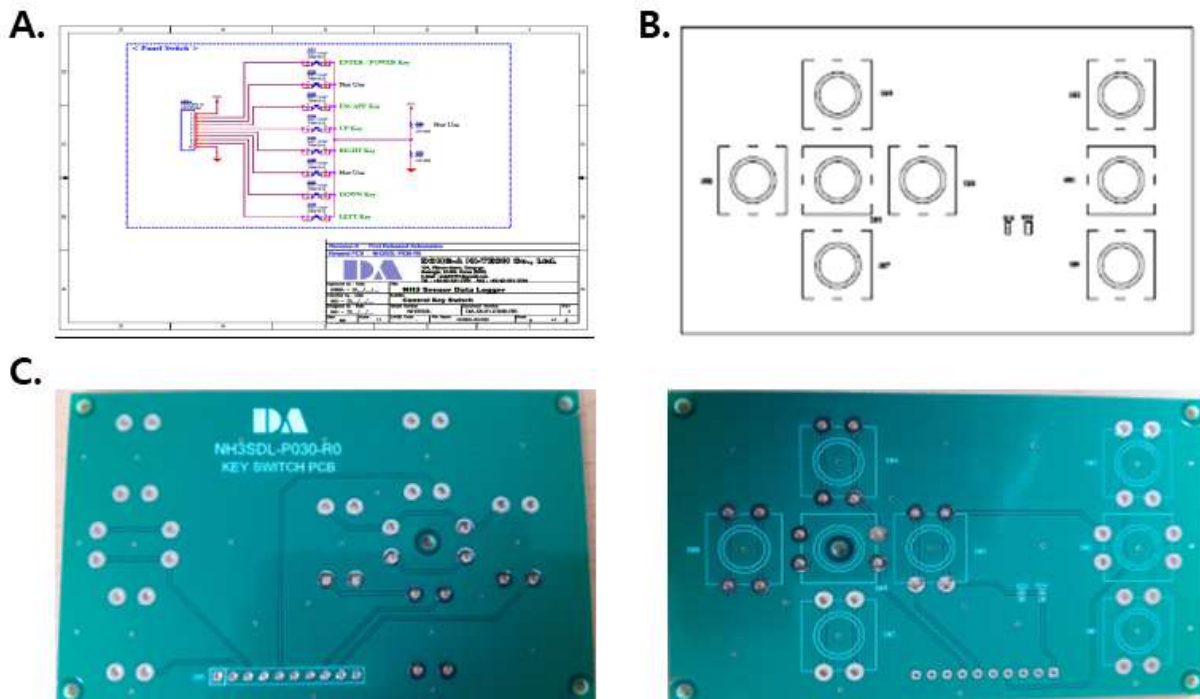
Key Switch 파트의 PCB. (A) Key Switch 파트 회로도, (B) Key Switch 파트 거버파일, (C) Key Switch 파트 PCB
